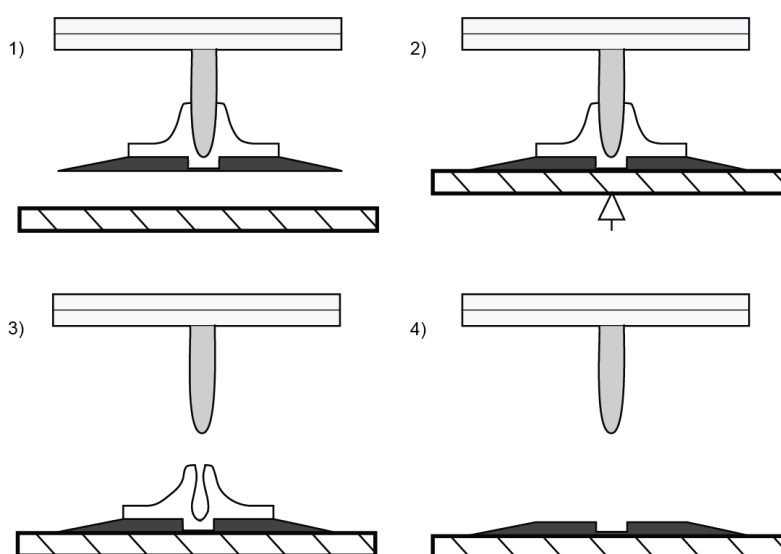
Процесс подготовки штанц-формы к высечке
